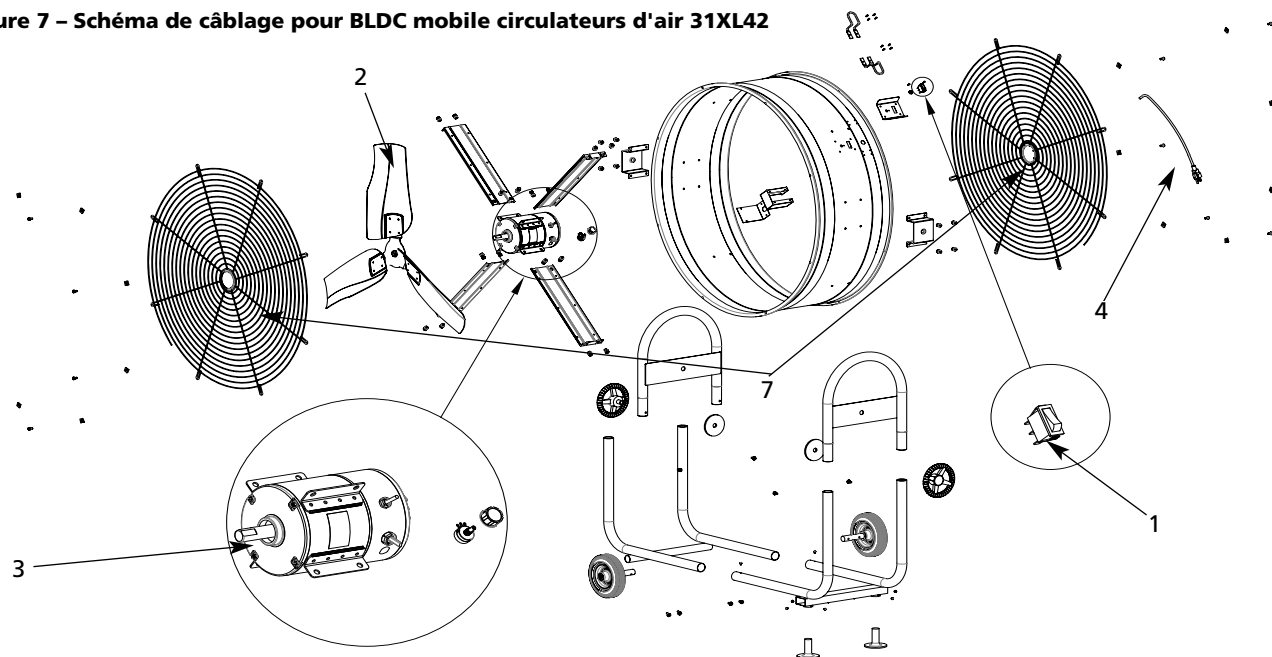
Illustration de Pièce de Réparation pour Circulateur de Air Mobile BLDC 31XL42
